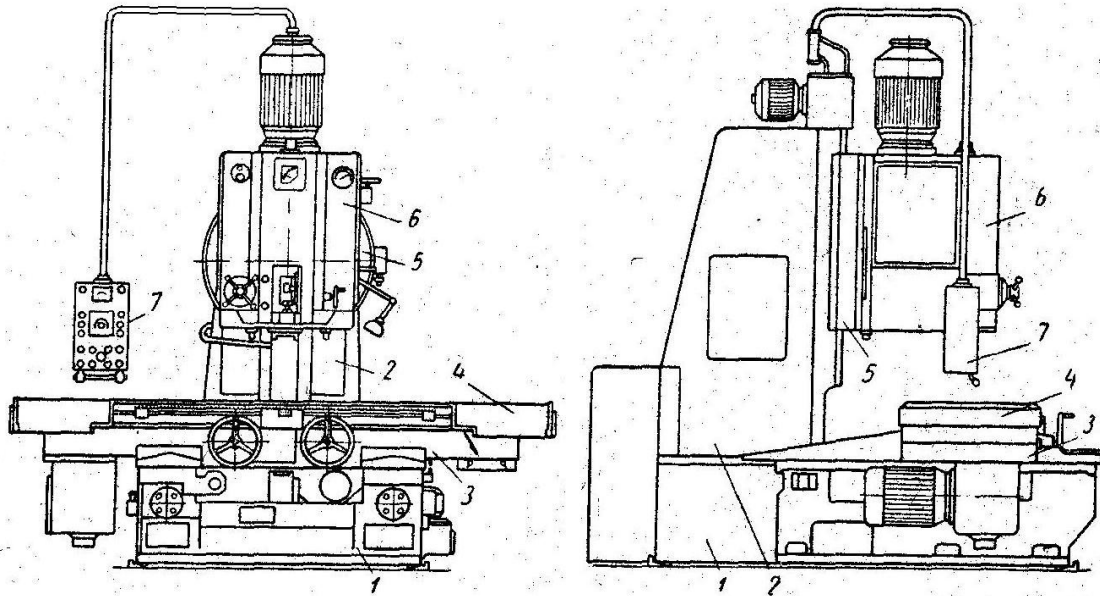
Загальний вигляд вертикально-фрезерного безконсольного верстата моделі 6560
